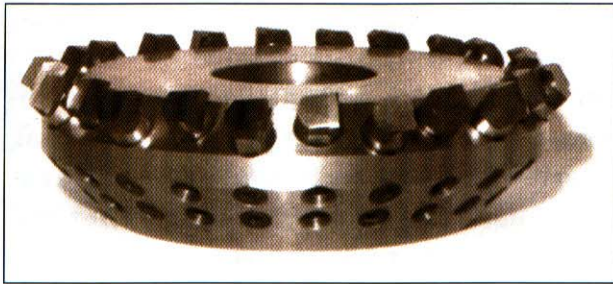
Торцовая фреза $\varnothing 200$ мм с напайными твердосплавными режущими вставками.
